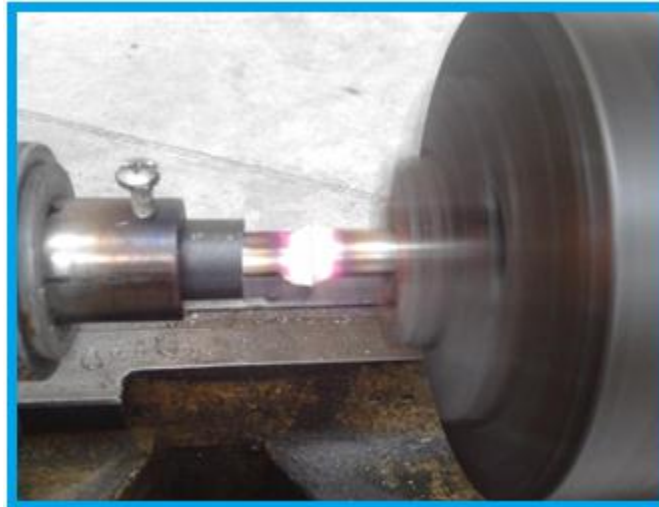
Montaje de las piezas a soldar, una en el cabezal del el torno y la otra en el extremo de nuestro pistón del mecanismo.
